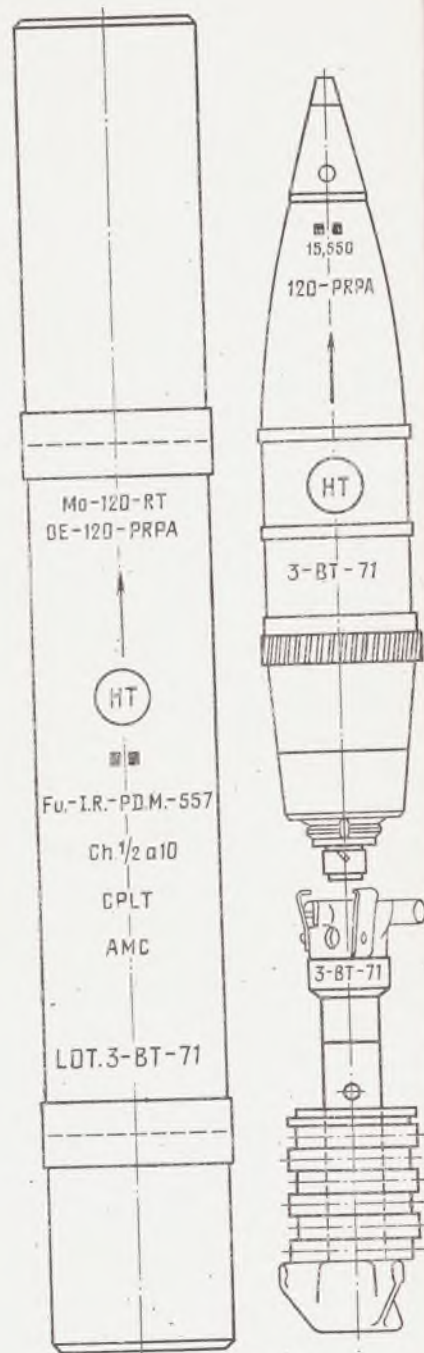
Образец маркировки активно-реактивного ОФ снаряда PRPA и укупорки для выстрела
